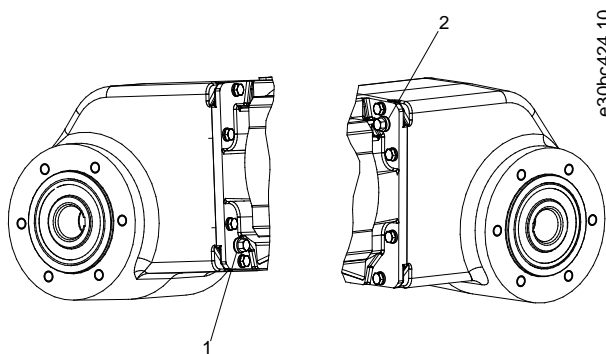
VLT® OneGearDrive® Ölschrauben 1 und 2
